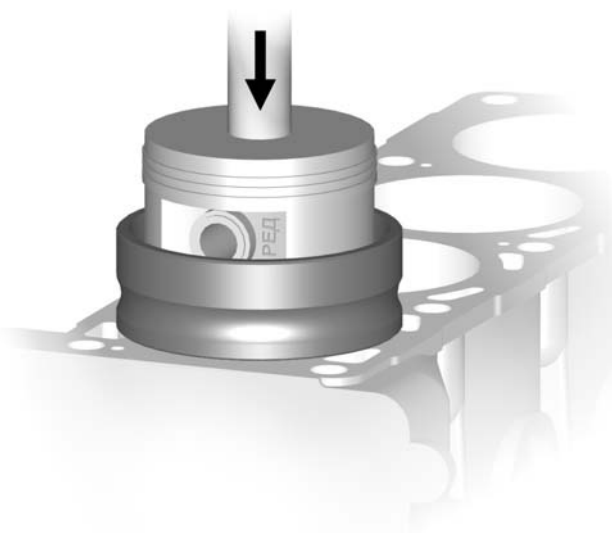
Установка поршня с кольцами в цилиндр при помощи оправки
